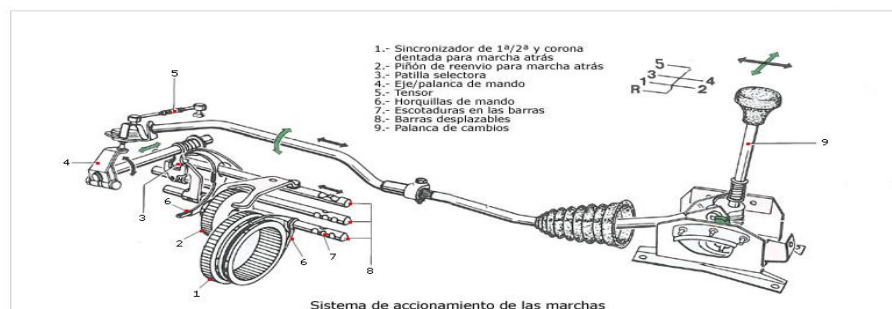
Sistema de varillaje de la caja de cambios²²
